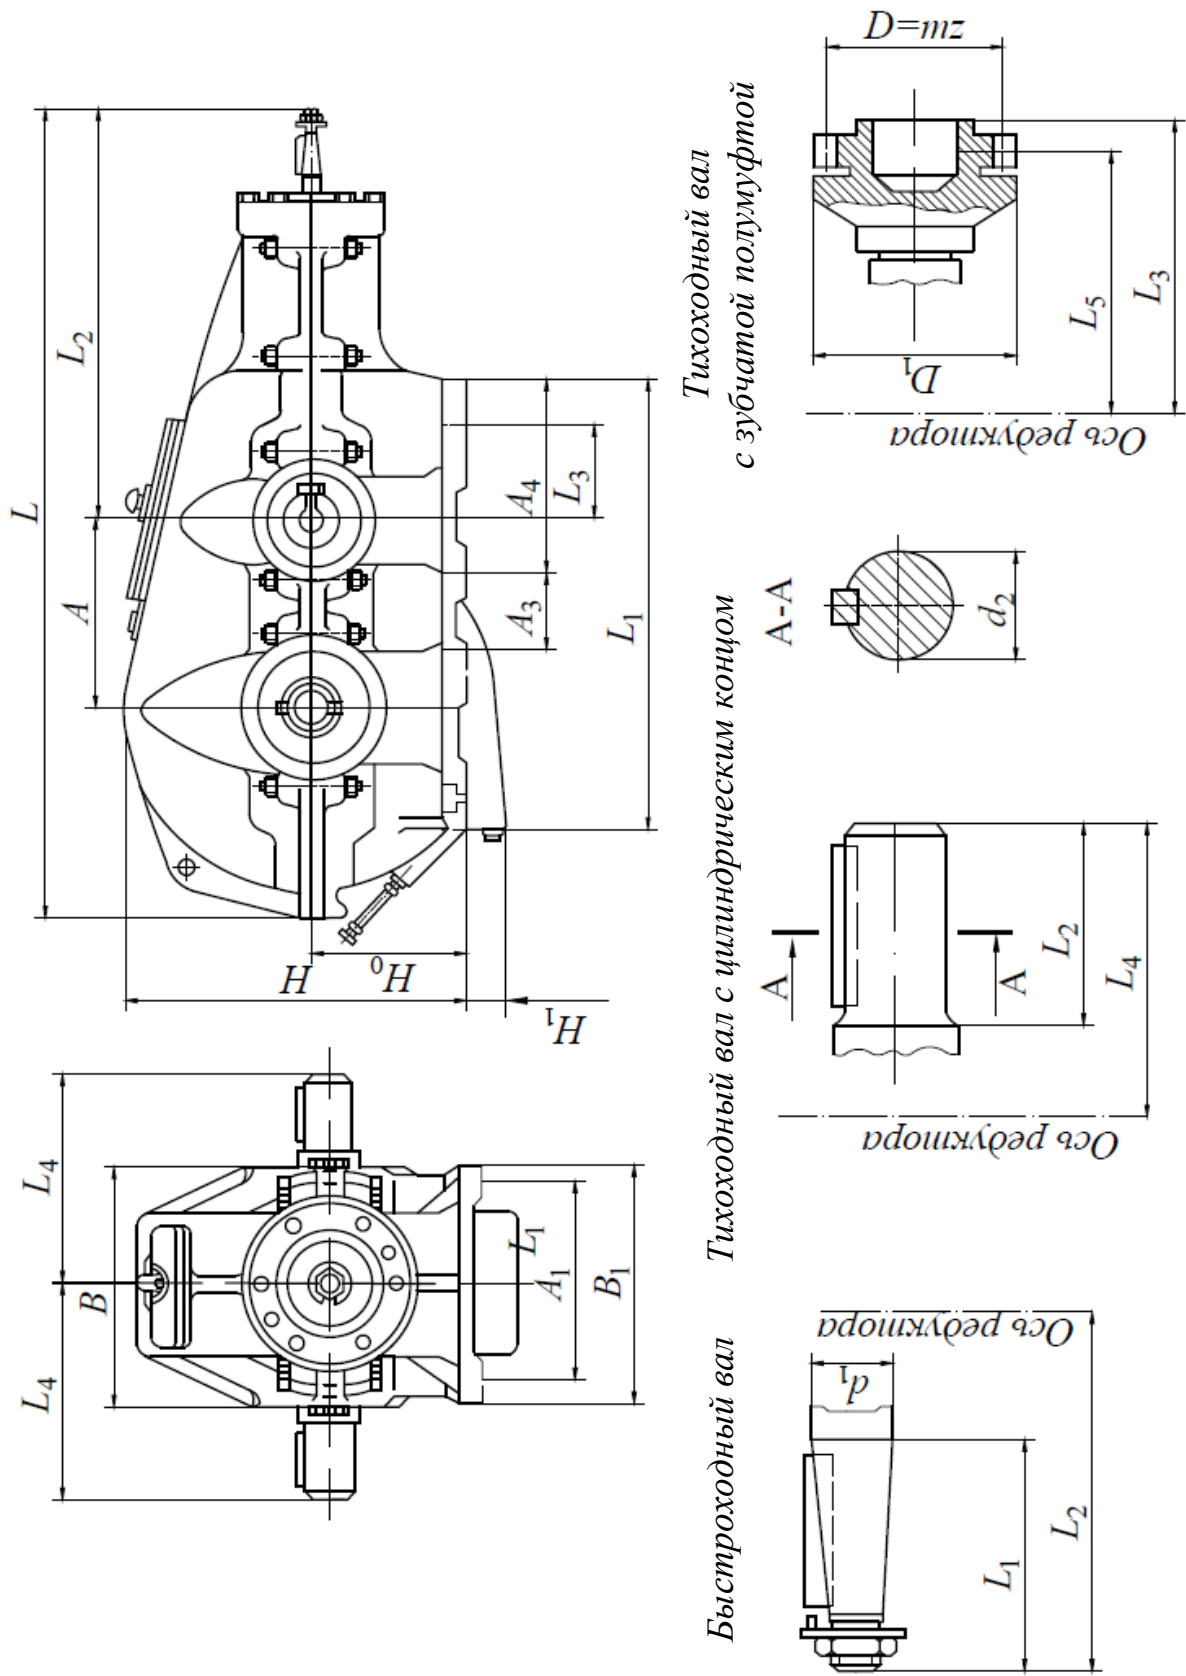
Редуктор двухступенчатый коническо-цилиндрический и концы валов
